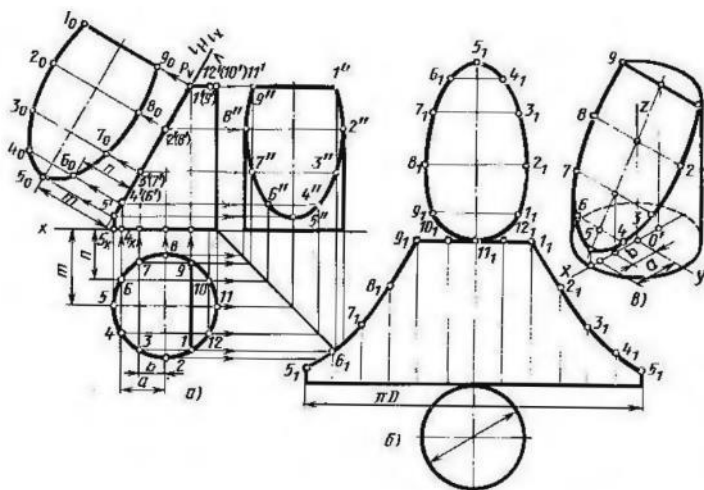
комплексный чертеж, изометрия и развертка цилиндра.
